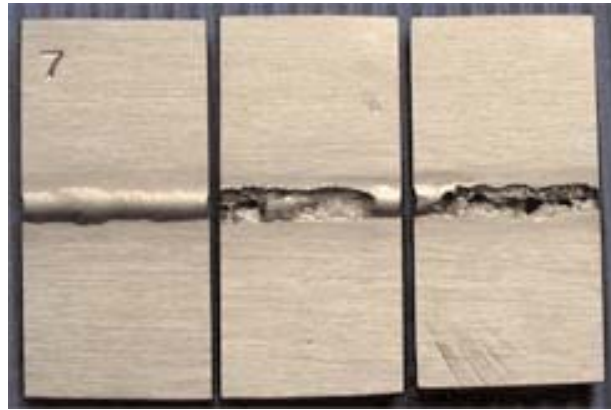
Inconel 622 soldado com o metal de adição de Inconel 622 (THORTON & COOPER, 2004).
